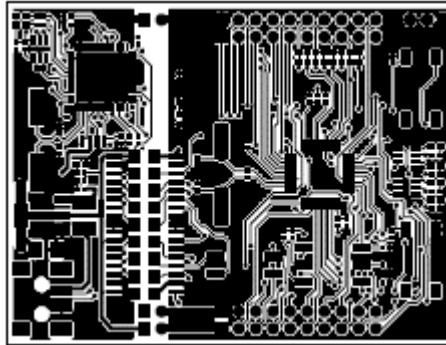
Disposition du PCB LAUNCHXL-F28027 - Couche supérieure
